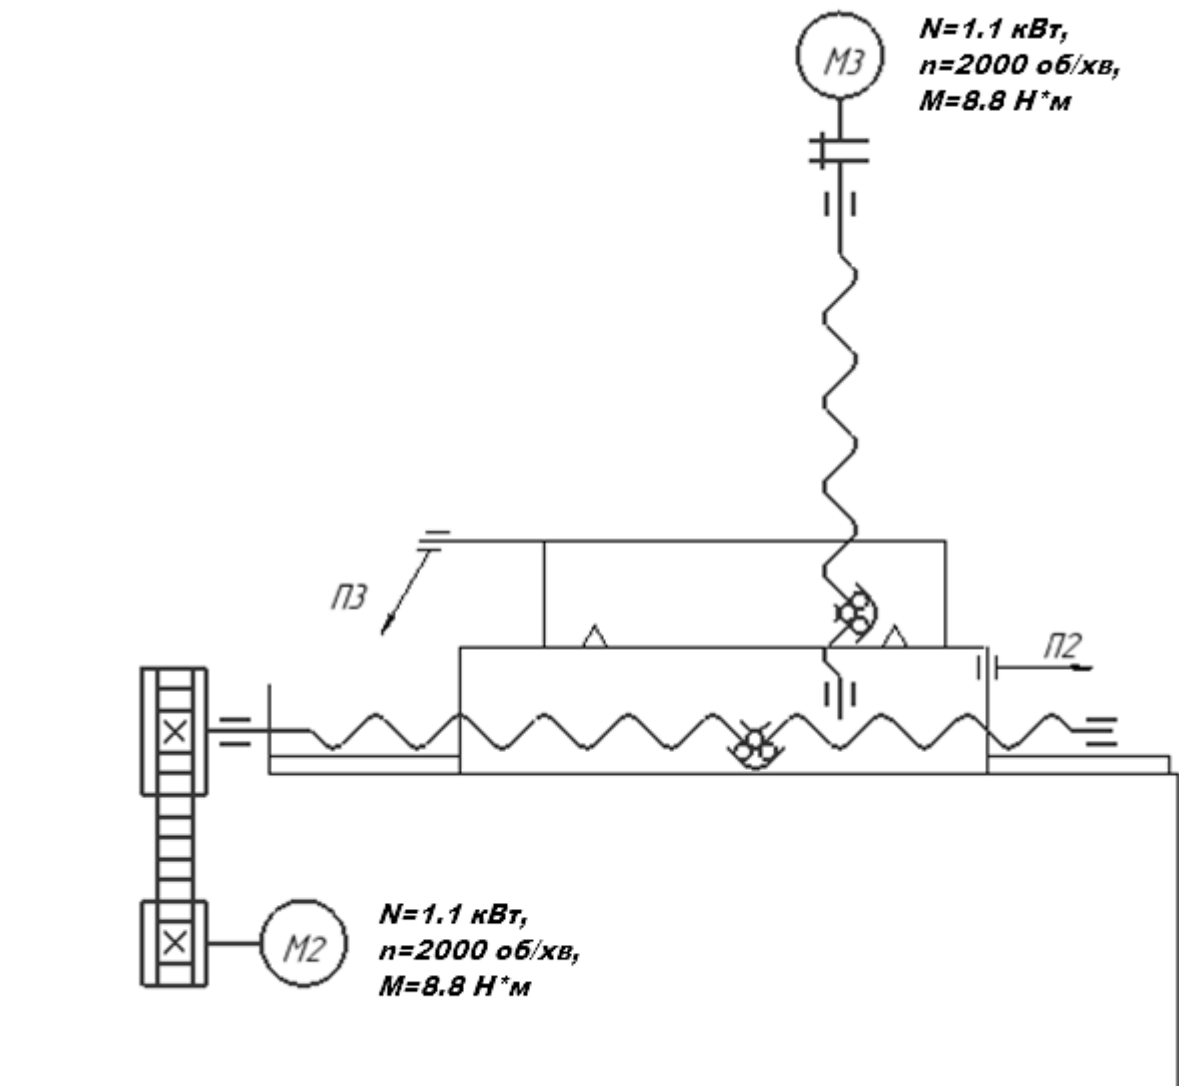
Розрахункова схема приводу хрестового супорта
